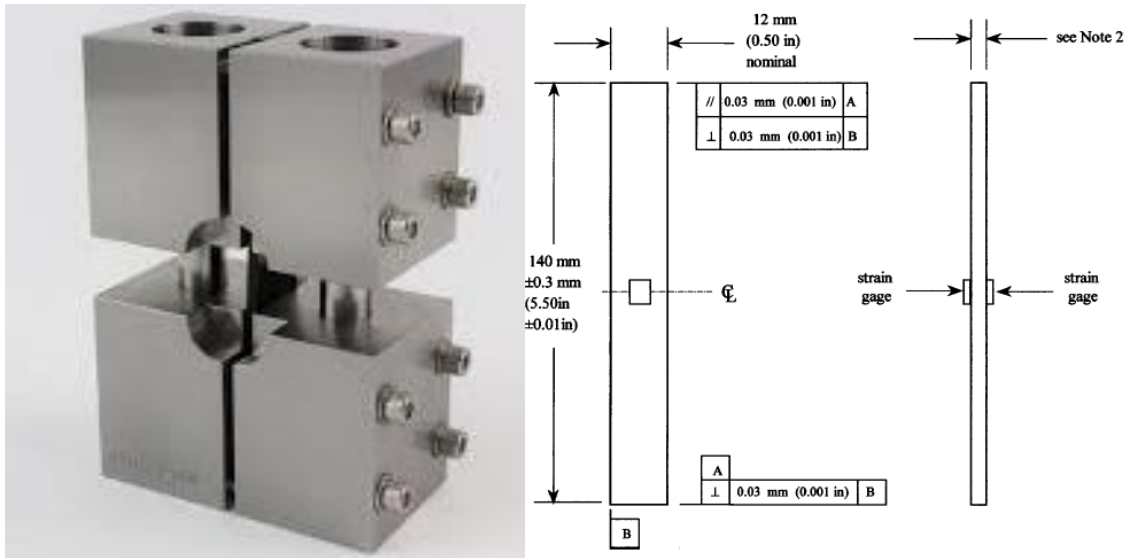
Чертеж образца и противоизгибное приспособление для ASTM D 6641
